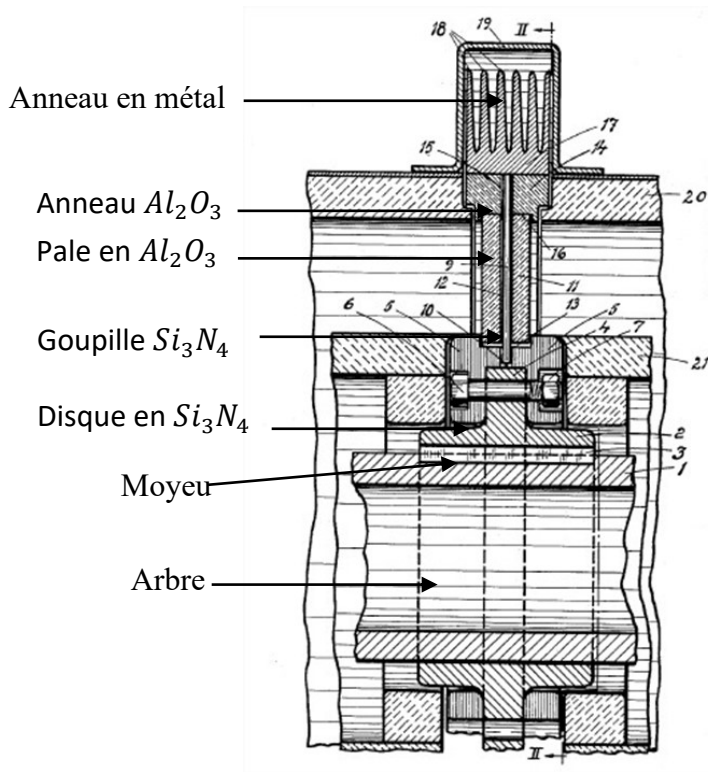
Dessin du rotor *Axial Flow Gas Turbine* inventé par Holmquist (vue de côté)
